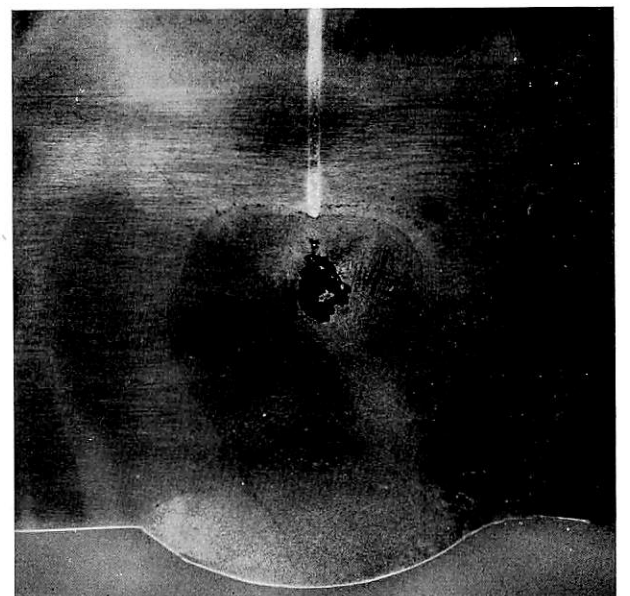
Kombinierte Schweißung, geglüht. Ätzung II.
